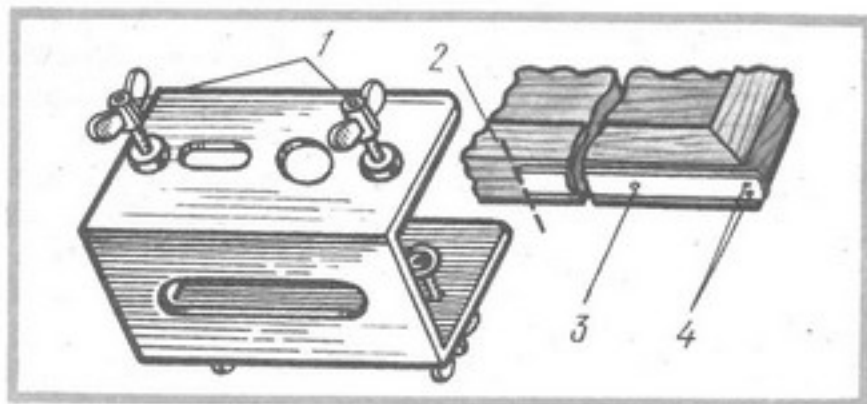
Кондуктор для выборки отверстий под замок в дверях:
